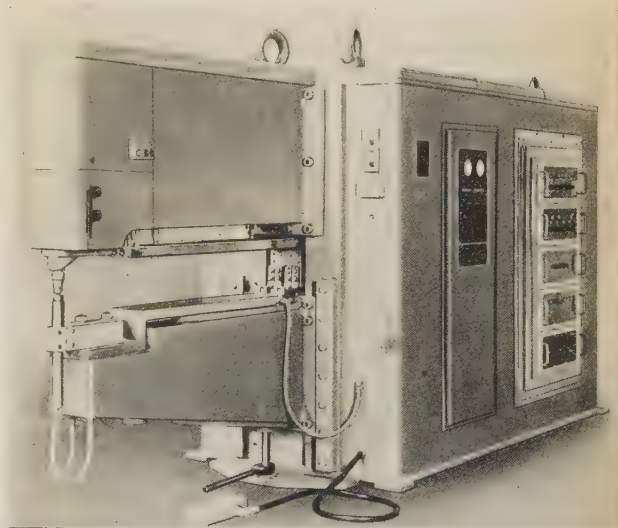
Dreiphasen-Hochleistungs-Punktschweißmaschine mit Ignitron-Symmetriertakter für maximale Blechstärken 2×3 mm
